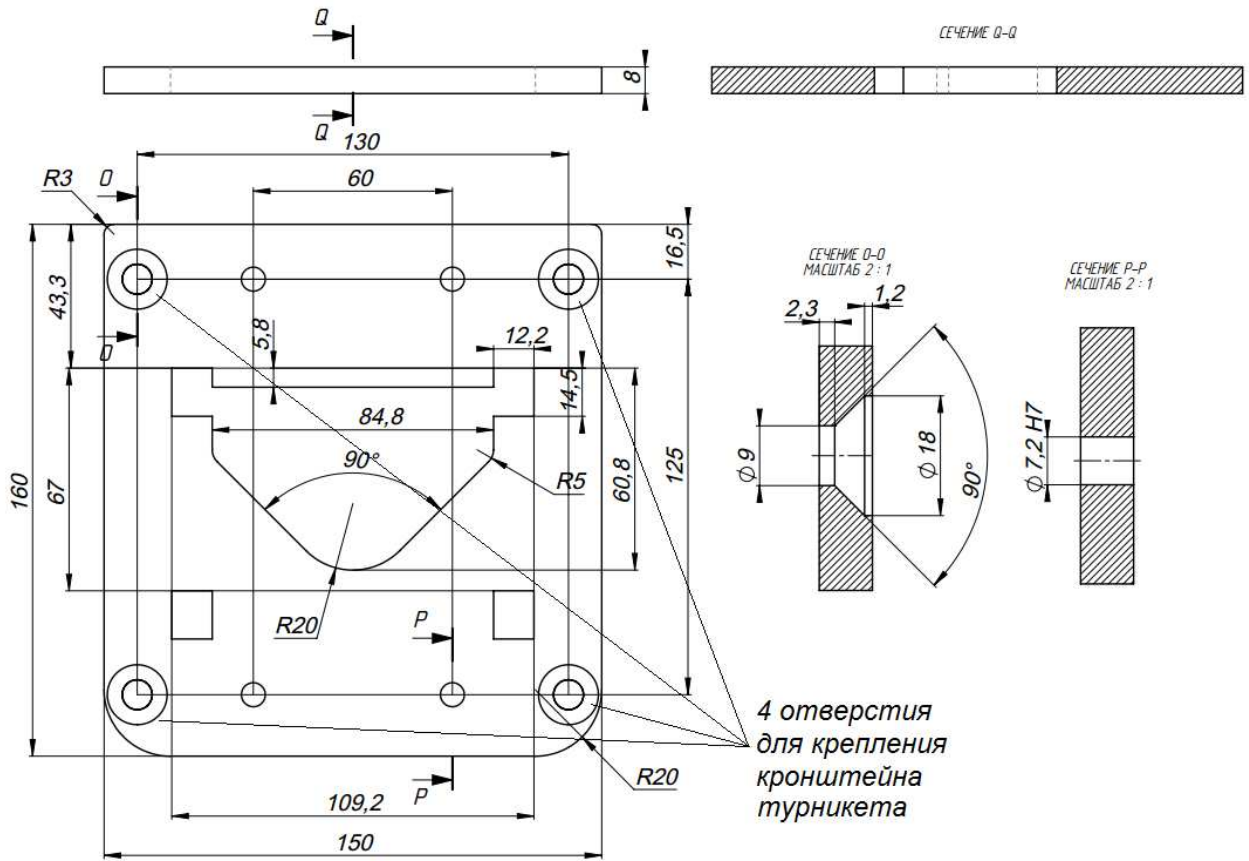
Установочные размеры (чертеж опоры крепления турникета на стену)
